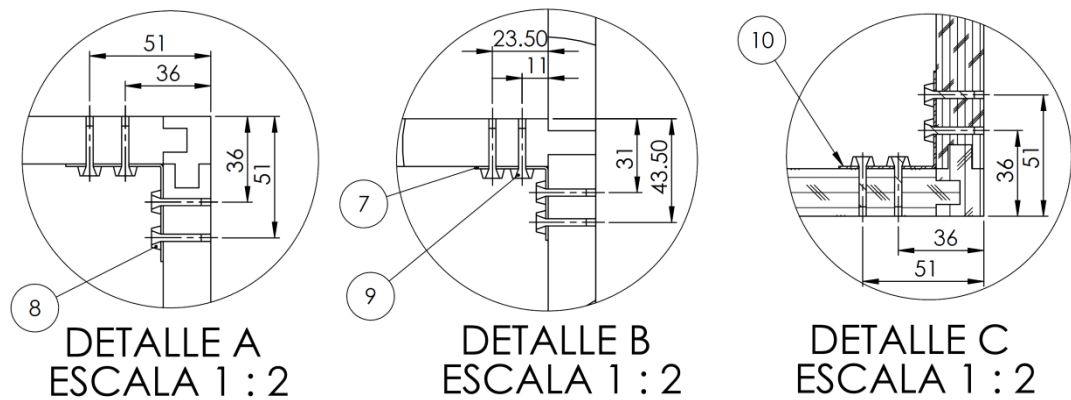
4: Vistas de detalles A, B y C del ensamble de la estructura. Fuente: Elaboración propia.
